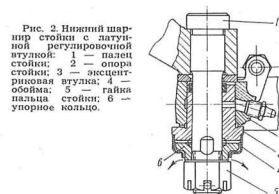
Нижний шарнир с латуниной регулировочной втулкой: 1 — палец стойки; 2 — опора стойки; 3 — эксцентриксовая втулка; 4 — обойма; 5 — гайка пальца стойки; 6 — упорное кольцо.
